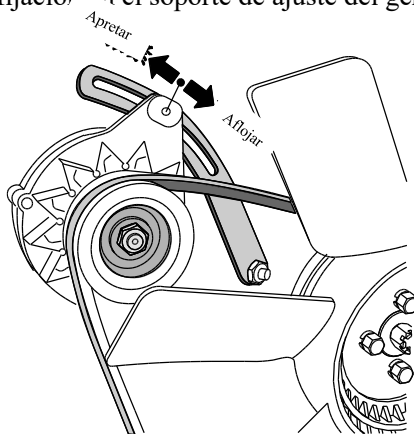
6 Inspección y ajuste de tensión de correa V de ventilador
